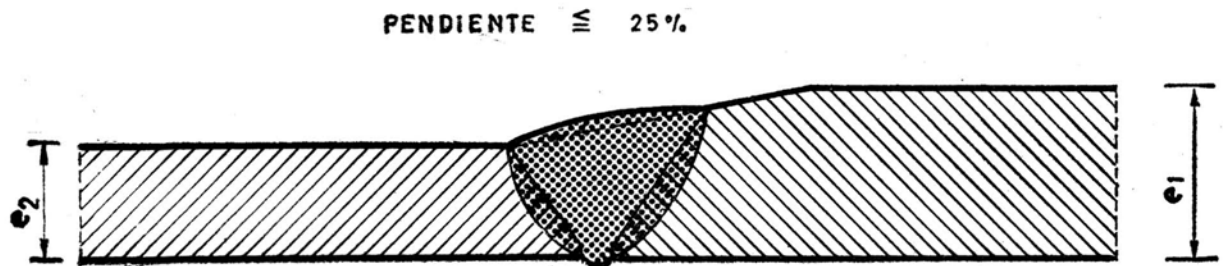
SOLDADURA A TOPE DE PIEZAS DE DISTINTA SECCION
